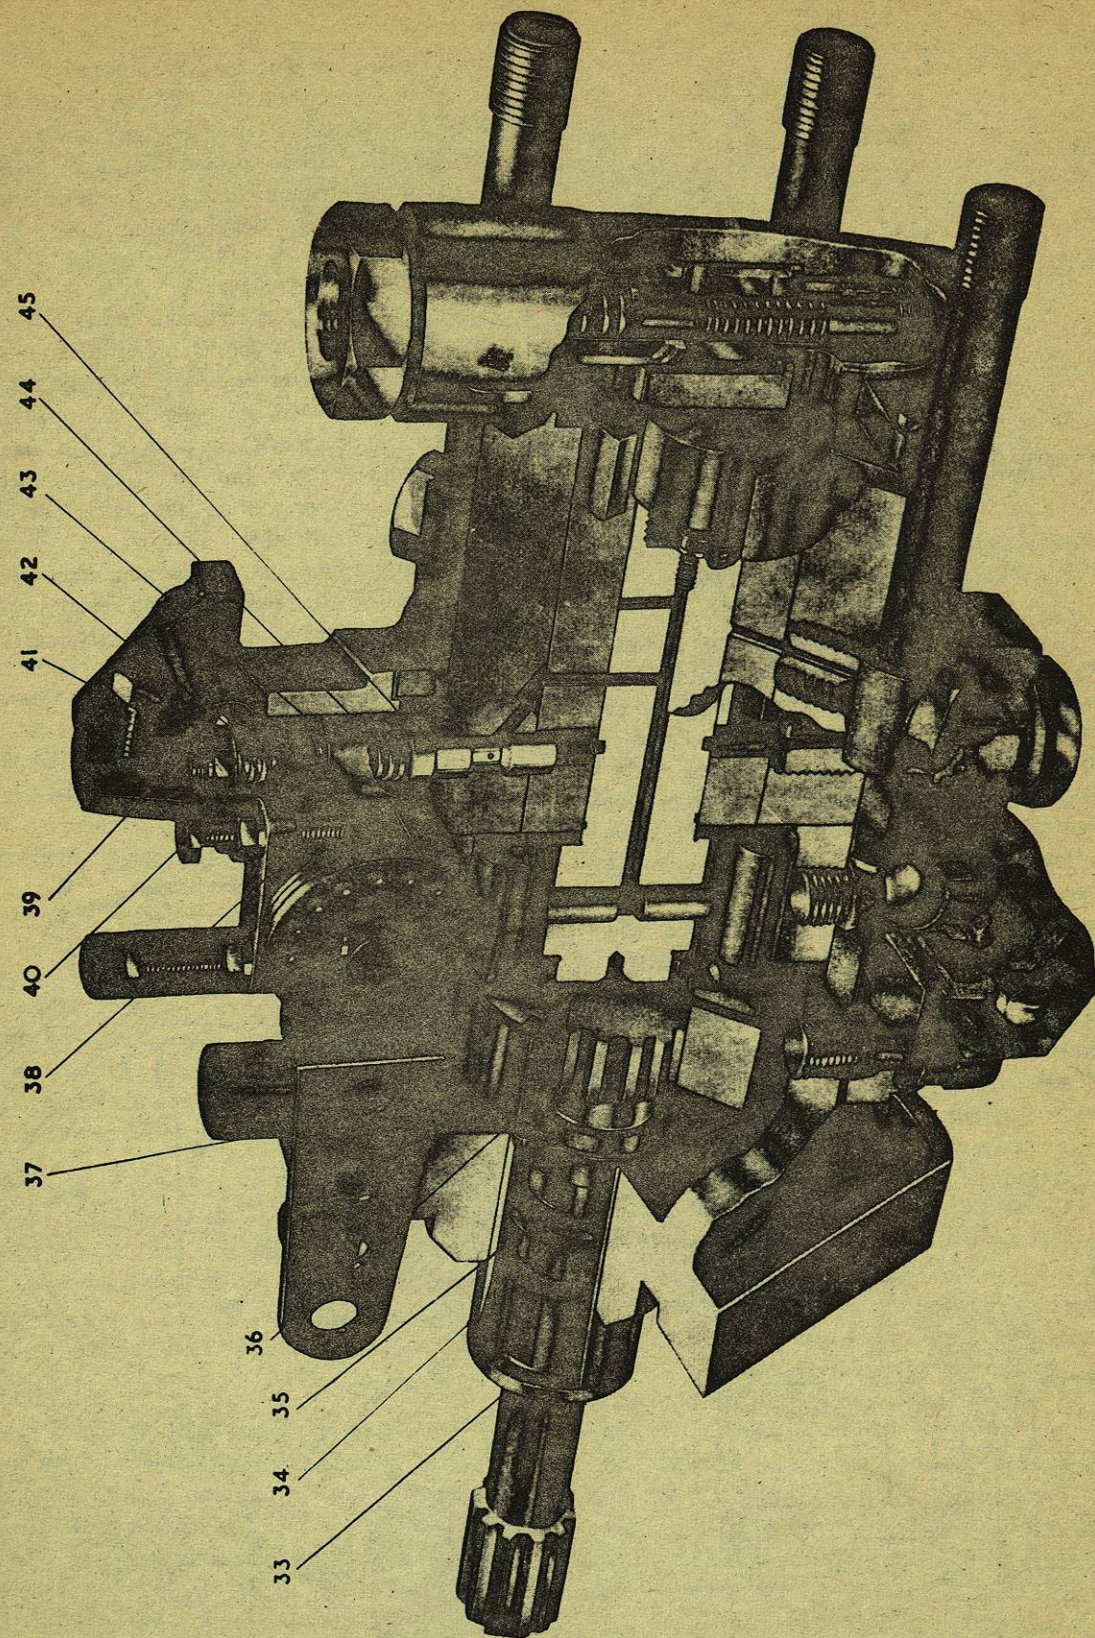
Bomba con regulador reversible y dispositivo de avance
